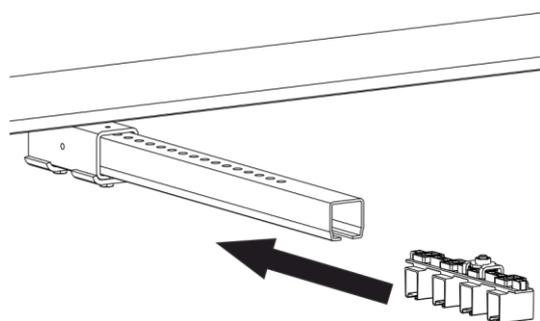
Pousser le support de rail compact dans un bras de serrage/rail C
